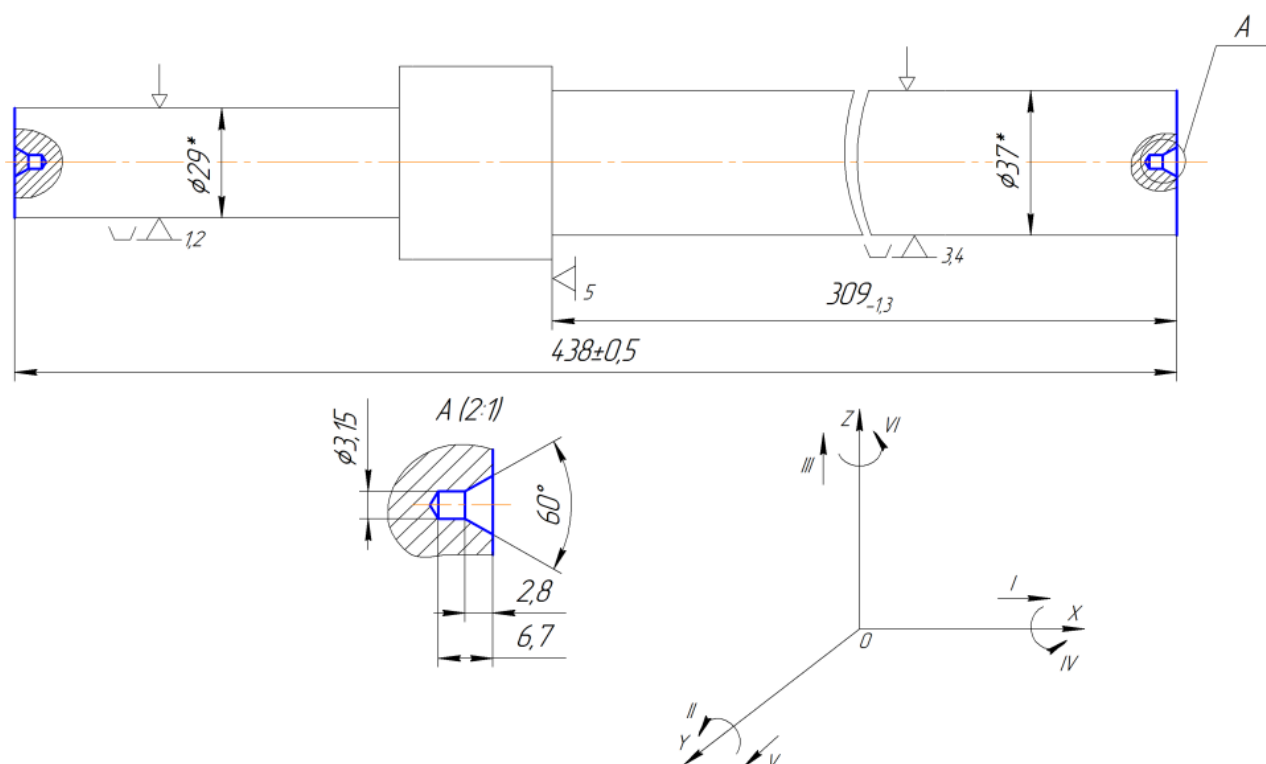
Схема базування деталі для фрезерно-центрувальної операції (варіант 1)
